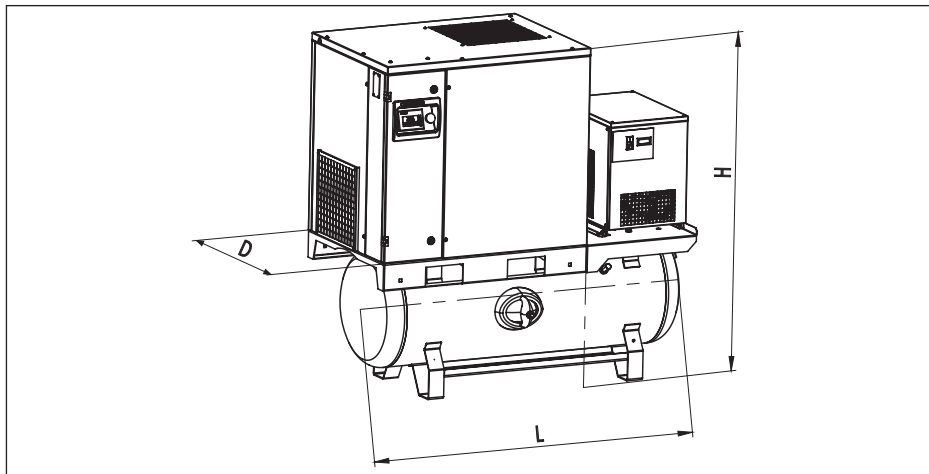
Размеры компрессора FR07..-FR22, FRD07..-FRD22.
